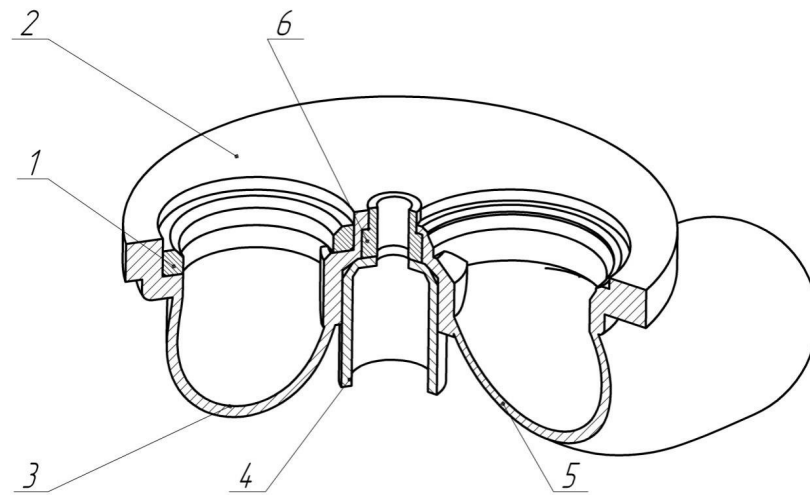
Армування форсункового отвору втулками з теплопровідного матеріалу: 1 – сідло клапана; 2 – теплоприймаюча поверхня вогневого днища головки блоку циліндрів; 3 – патрубок випускного клапана; 4 – форсунковий стакан; 5 – патрубок впускного клапана; 6 – втулка з теплопровідного матеріалу.
